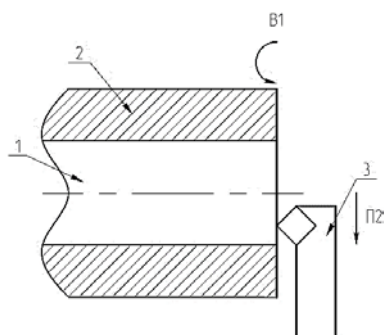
Схема точения торца заготовки при перемещении резца от оси вращения заготовки наружу
